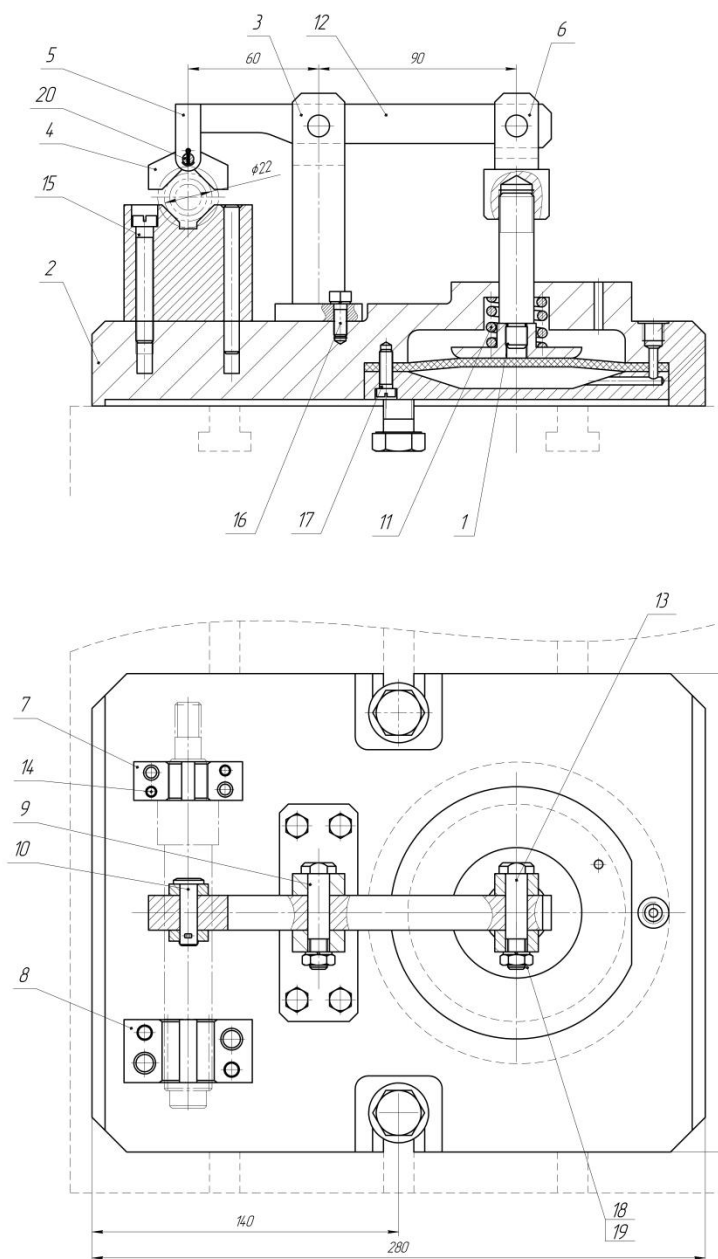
Компоновка (общий вид) приспособления показан на чертеже.
